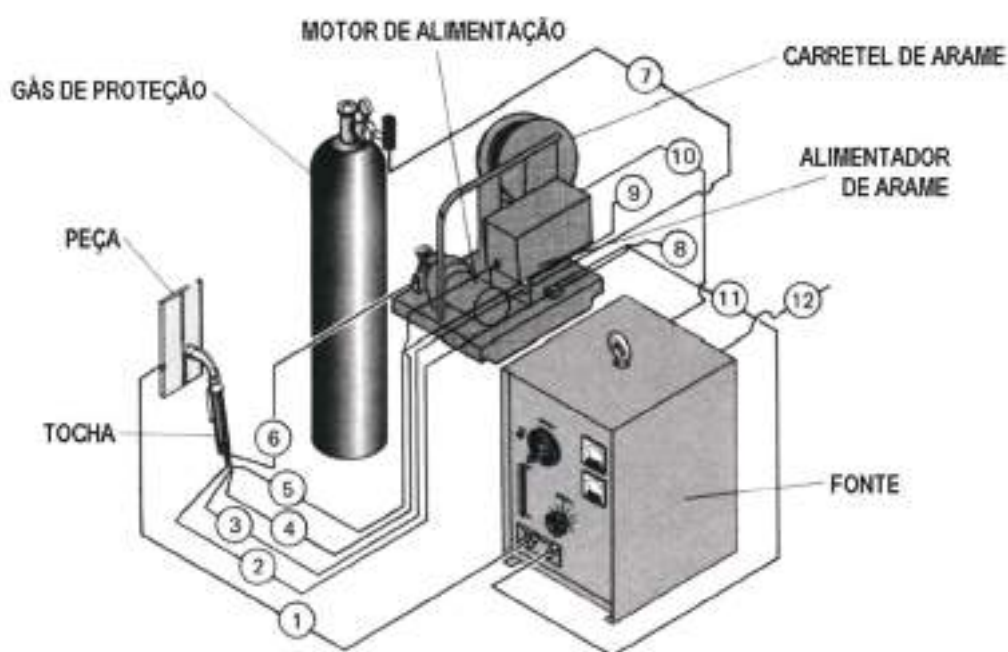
Instalações para a soldadura manual: 1. Cabo de solda (negativo); 2. Refrigeração da tocha (água); 3. Gás de proteção; 4. Gatilho da tocha; 5. Água de refrigeração para a tocha; 6. Condutor do arame; 7. Gás de proteção vindo do cilindro; 8. Saída de água de refrigeração; 9. Entrada de água de refrigeração; 10. Entrada de 42 v (CA); 11. Cabo de solda (positivo); 12. Conexão para a fonte primária (220/380/440 V).
